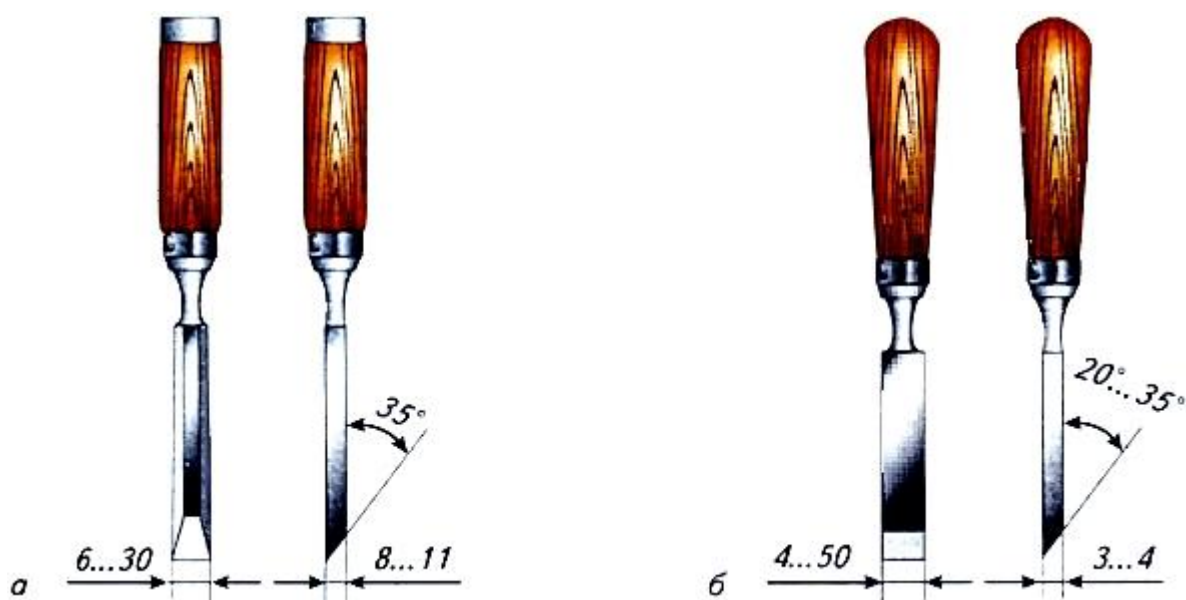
Инструменты для выдалбливания проушин: а — долото; б — стамеска
